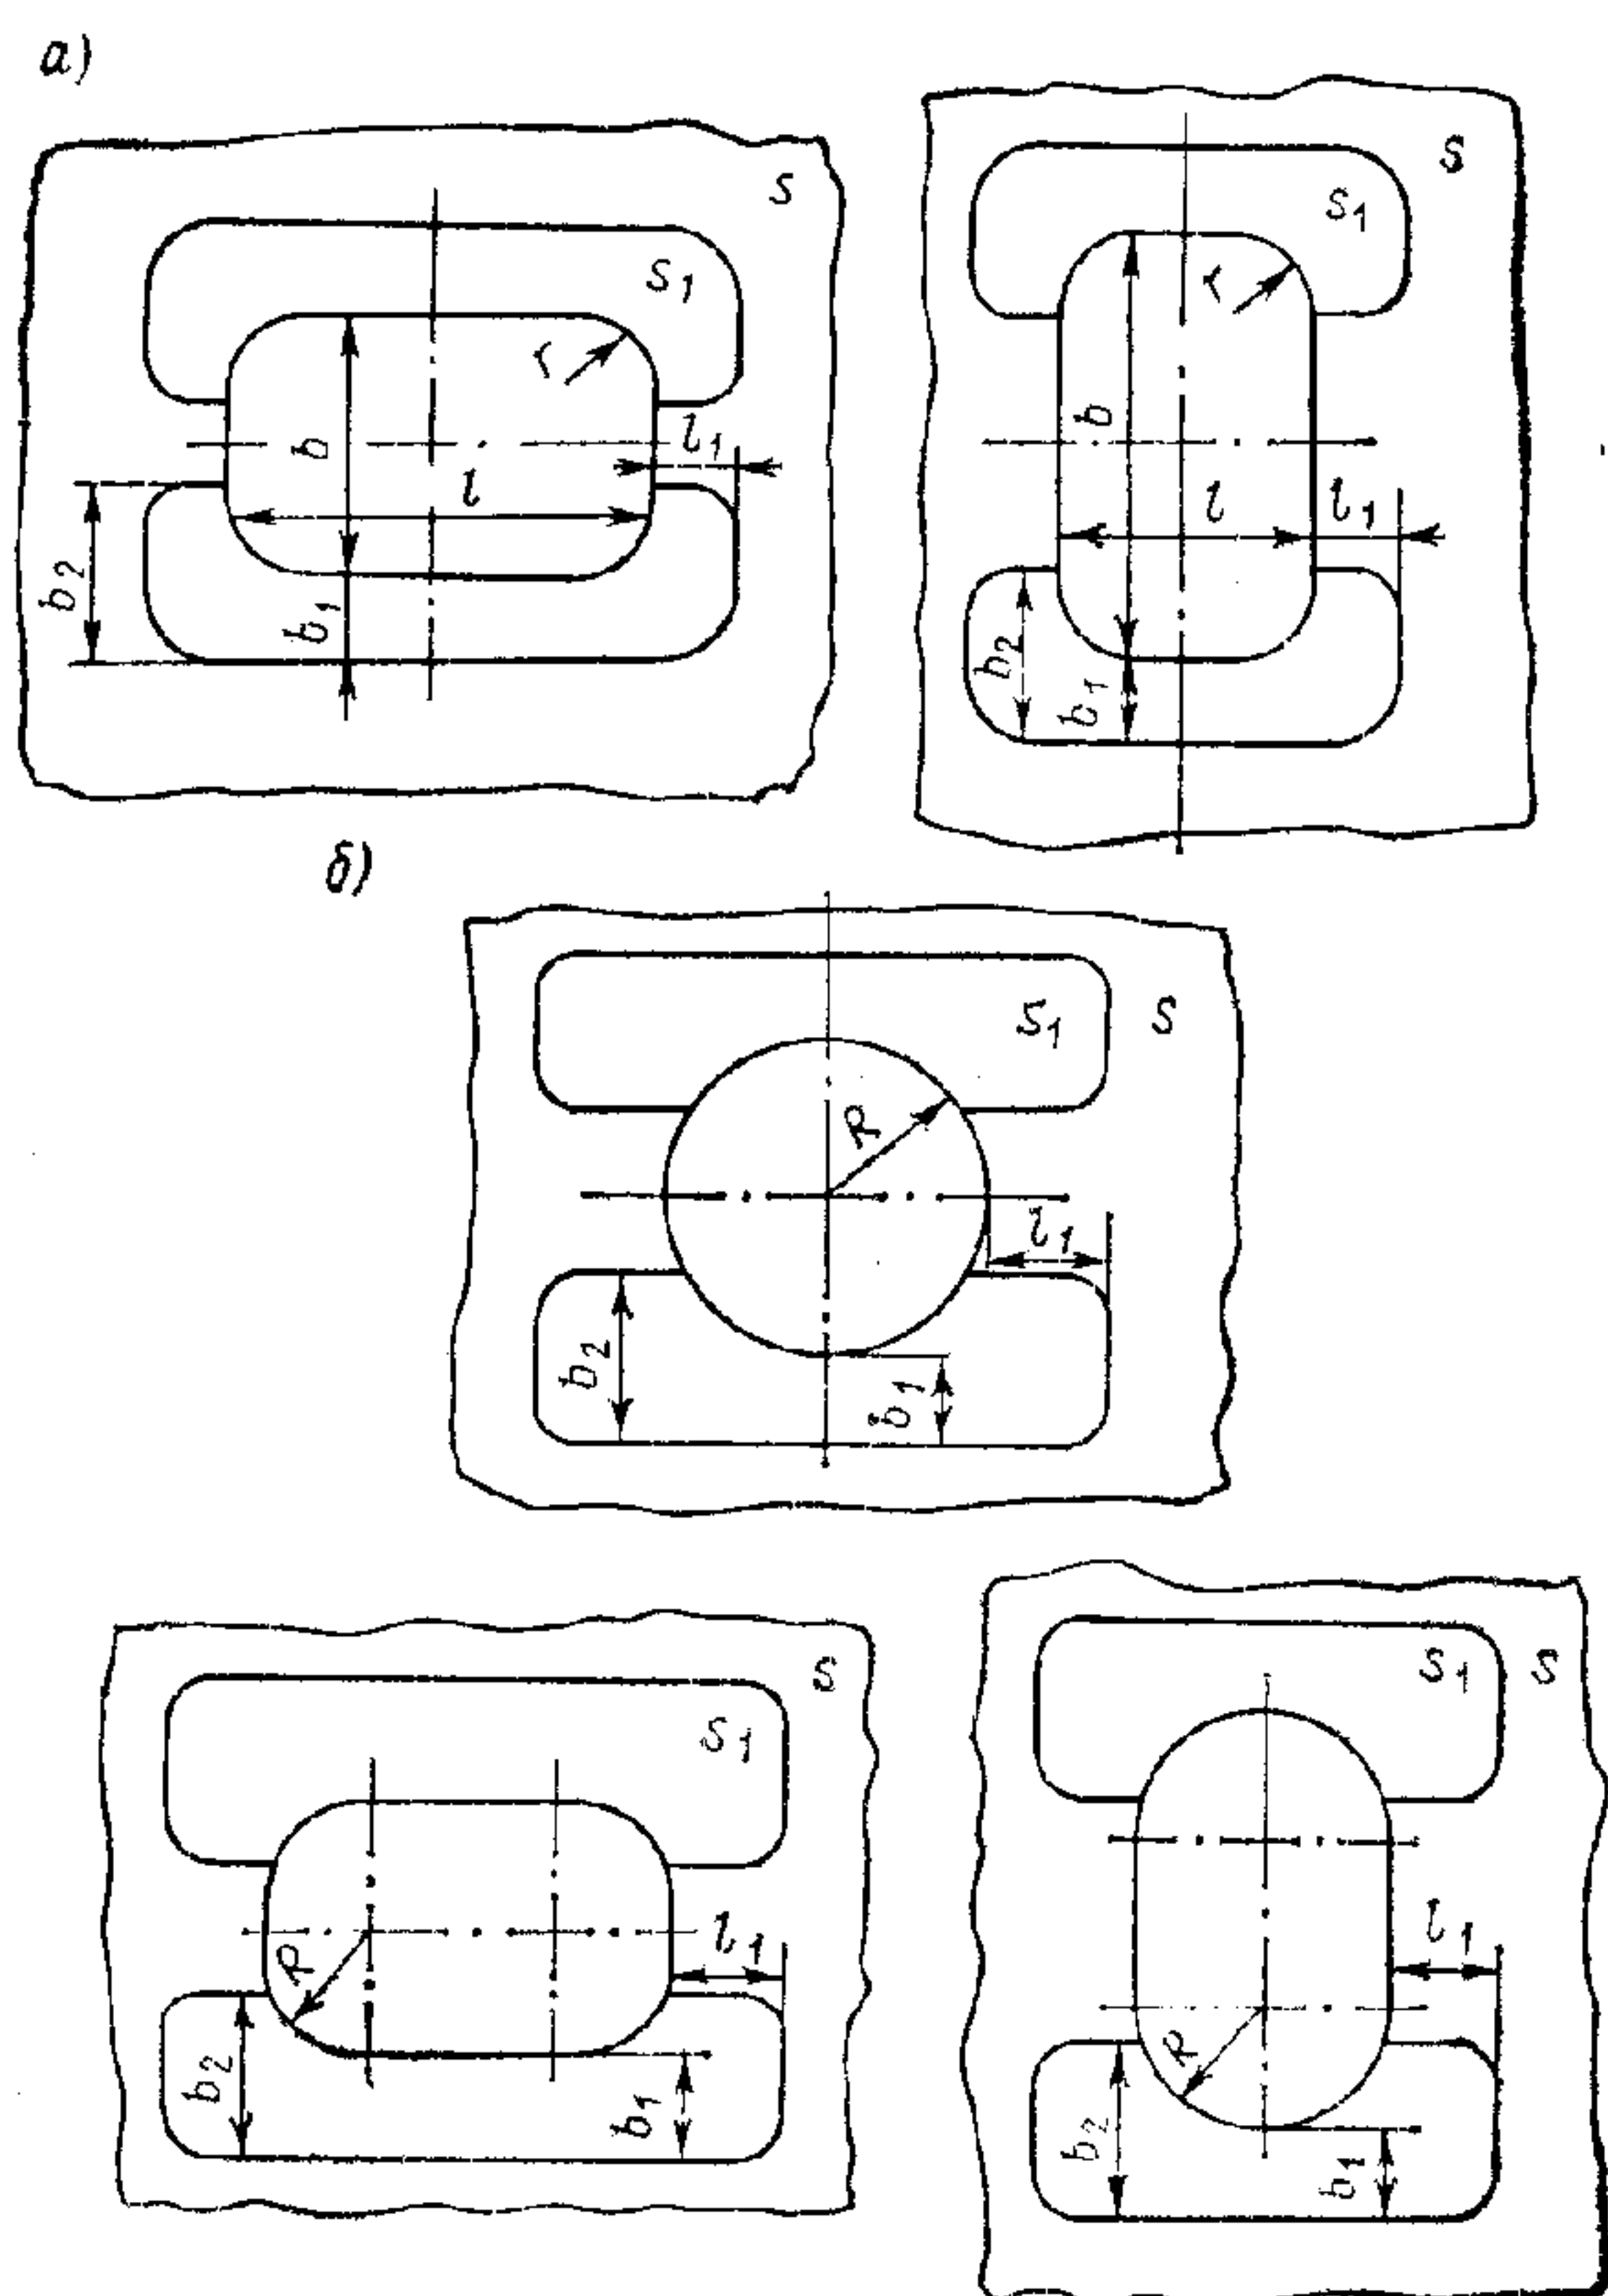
Подкрепление прямоугольных (а), круглых и овальных (б) вырезов в бортах утолщенными сварными листами
